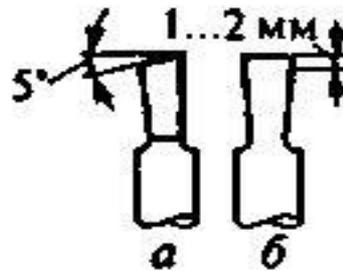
Отрезные резцы а- для получения ровного торца у отрезаемой детали; ; б- для уменьшения шероховатости
